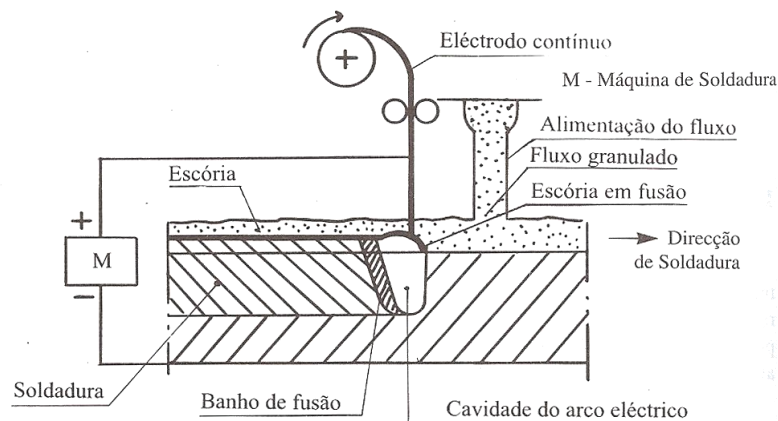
Princípio do processo de soldadura por arco submerso [9]
